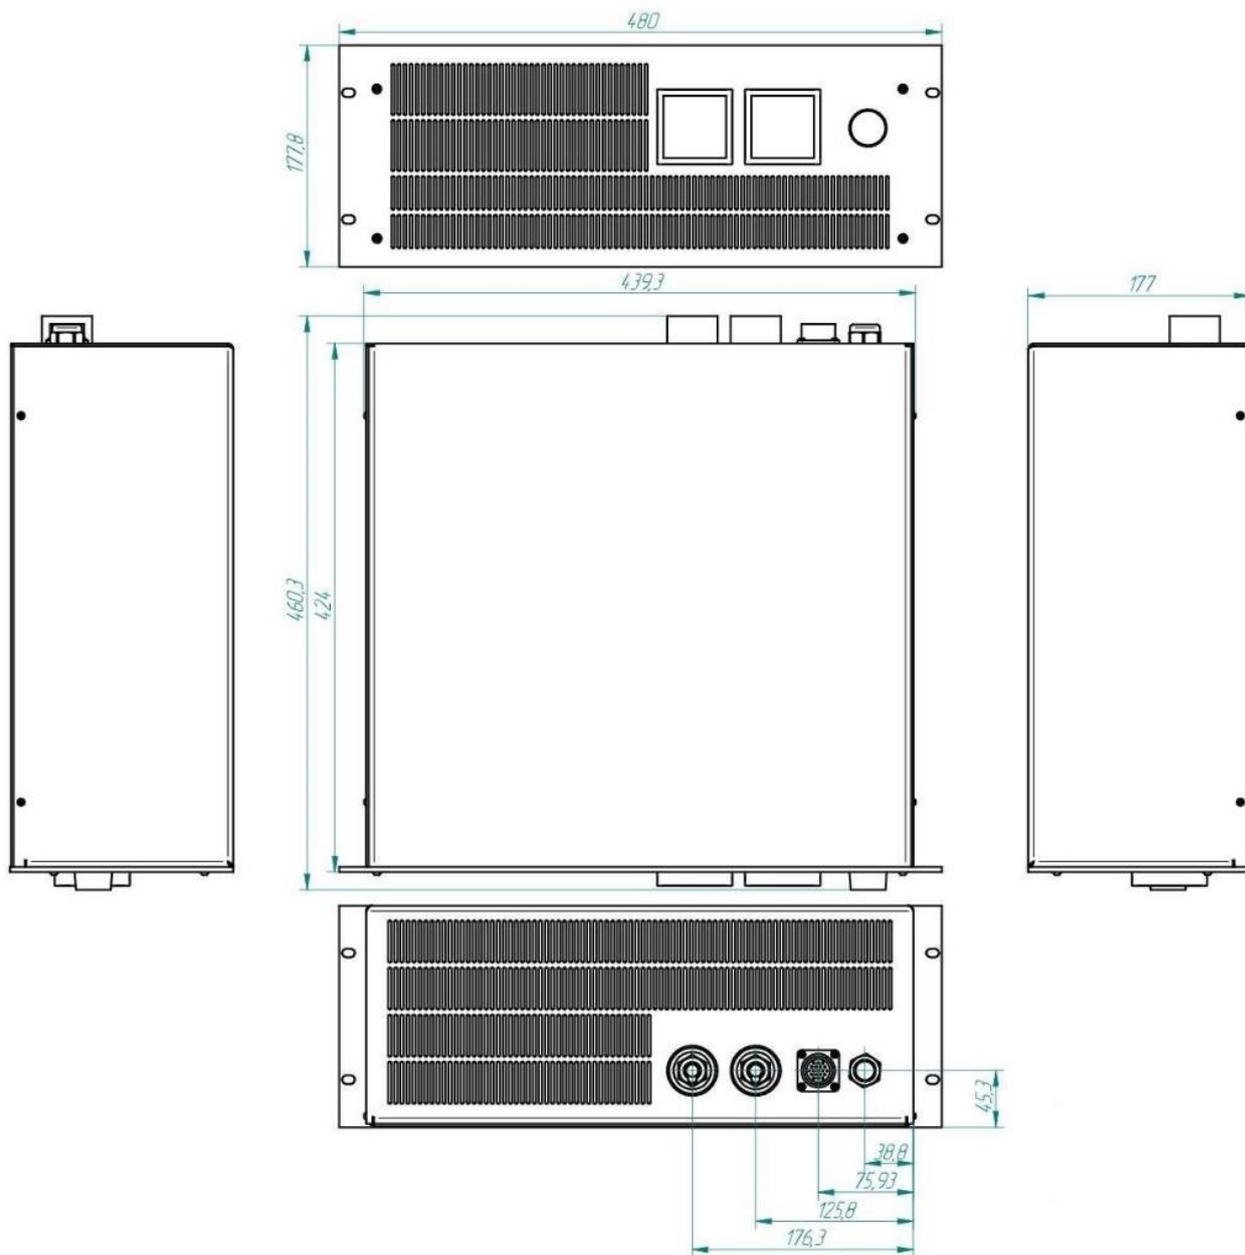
Габаритные и установочные размеры сварочного аппарата
